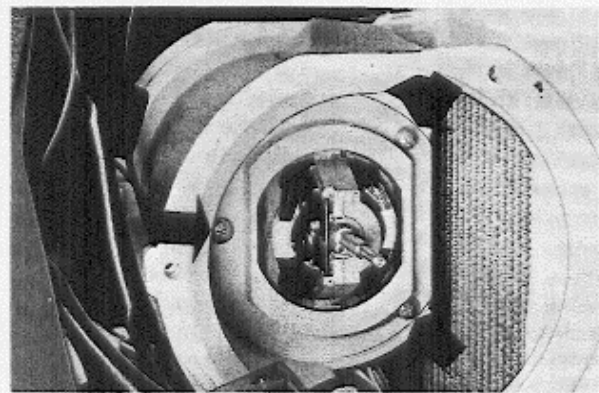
Befestigungsschrauben für Trägergehäuse des Gebläse motors
